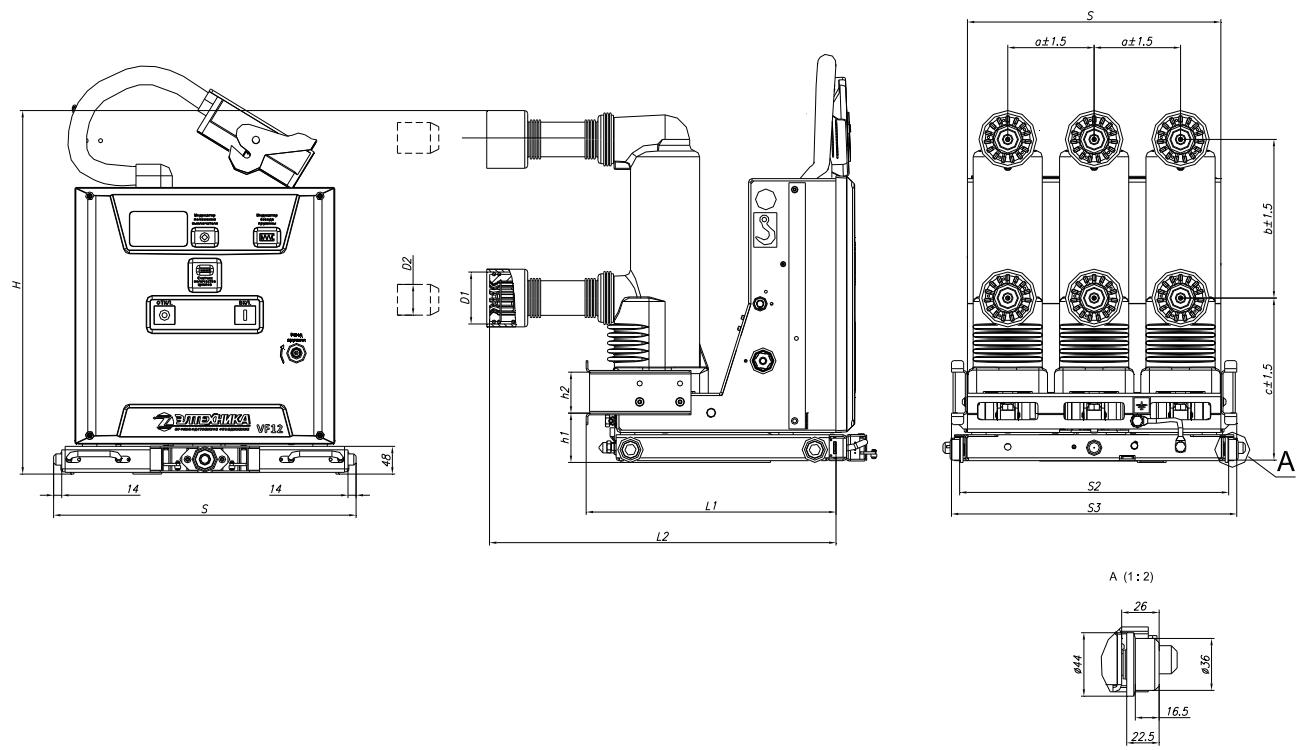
Габаритно-присоединительные размеры выключателей в исполнении S на токи 630–1250 А с механической блокировкой внешних устройств:
